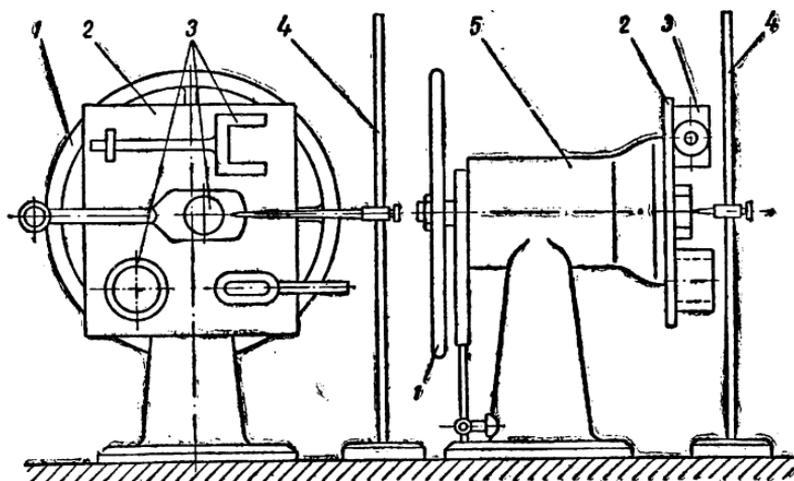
Электромагнитная плита для разметки заготовок: 1—колесо; 2—плита; 3—детали; 4—рейсмус; 5—шпindelь установки.
